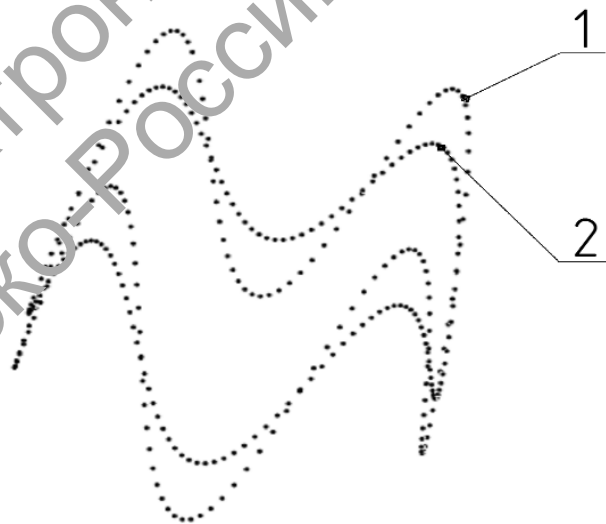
Траектории движения центра сферической фрезы: 1 – при фрезеровании профиля торцевой поверхности кулачка; 2 – при фрезеровании галтелей
